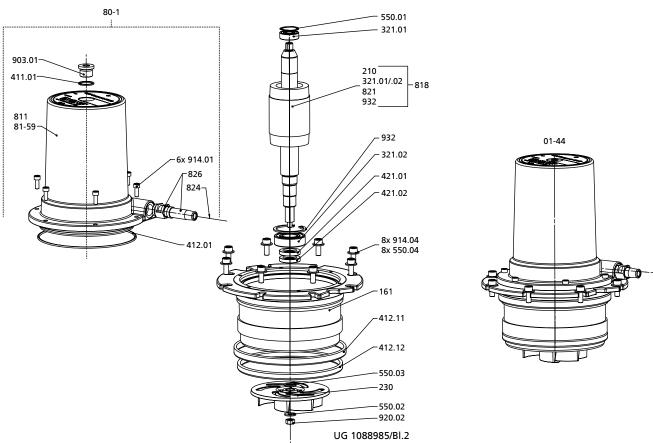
Покомпонентный сборочный чертеж mini-Compacta U60, U100, UZ150 — рабочая часть
